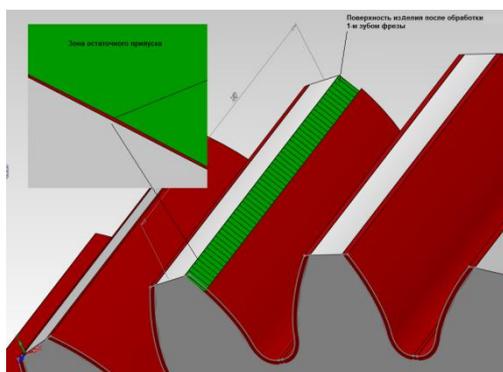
Формирование поверхности изделия после обработки первым зубом фрезы по всей длине зубчатого колеса
